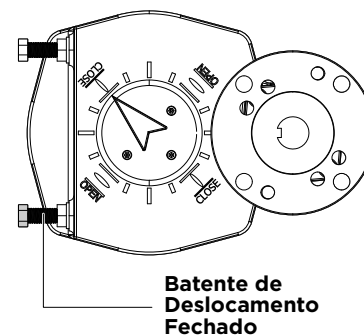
Posição da caixa de engrenagem FECHADA.
